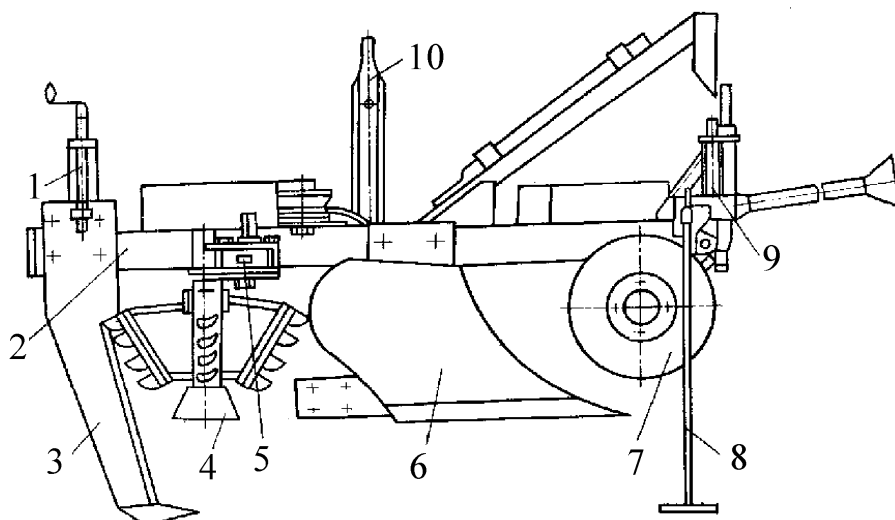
Плуг-рыхлитель ПРН-40: 1 – винт регулировки глубокорыхлителя; 2 – рама; 3 – глубокорыхлительная лапа; 4 – рыхлитель ротационный; 5 – механизм регулировки рыхлителя; 6 – корпус лемешный; 7 – дисковый подрезной нож; 8 – стойка; 9 – винт регулировки ножа; 10 – винт опорного колеса
